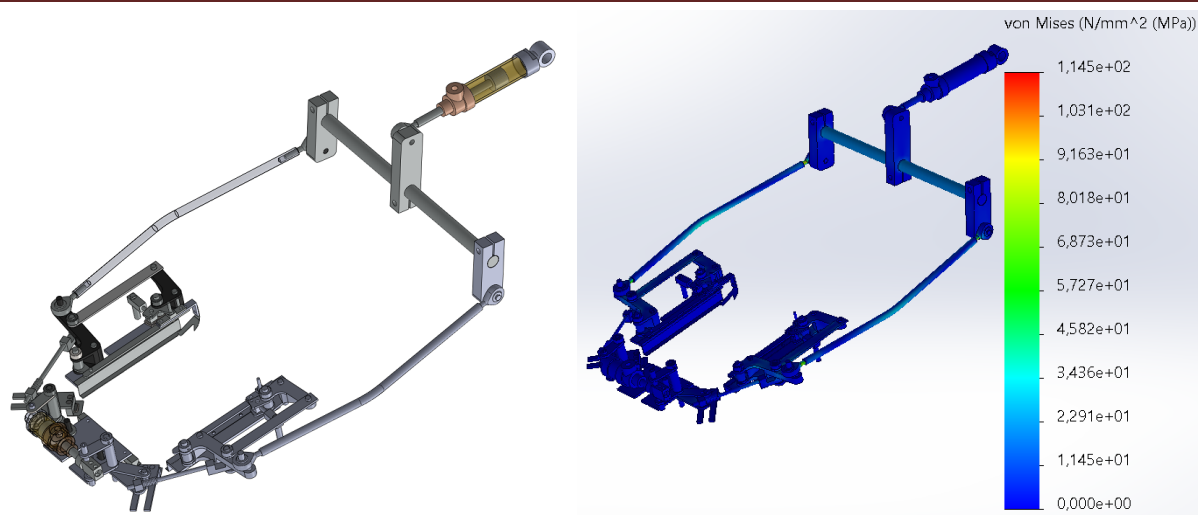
Механізм формування накладних кишень Durkopp-Adler 804: а – 3D модель створена в SoldsWorks, б – епюри напружень
